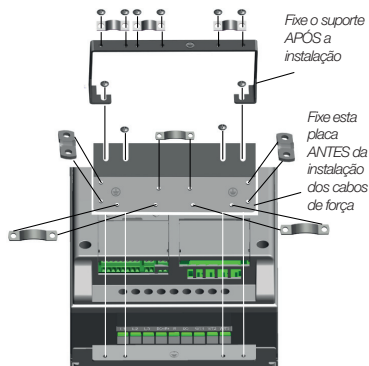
Instalação da placa PE e suporte a cabo API, MI4 - MI5
